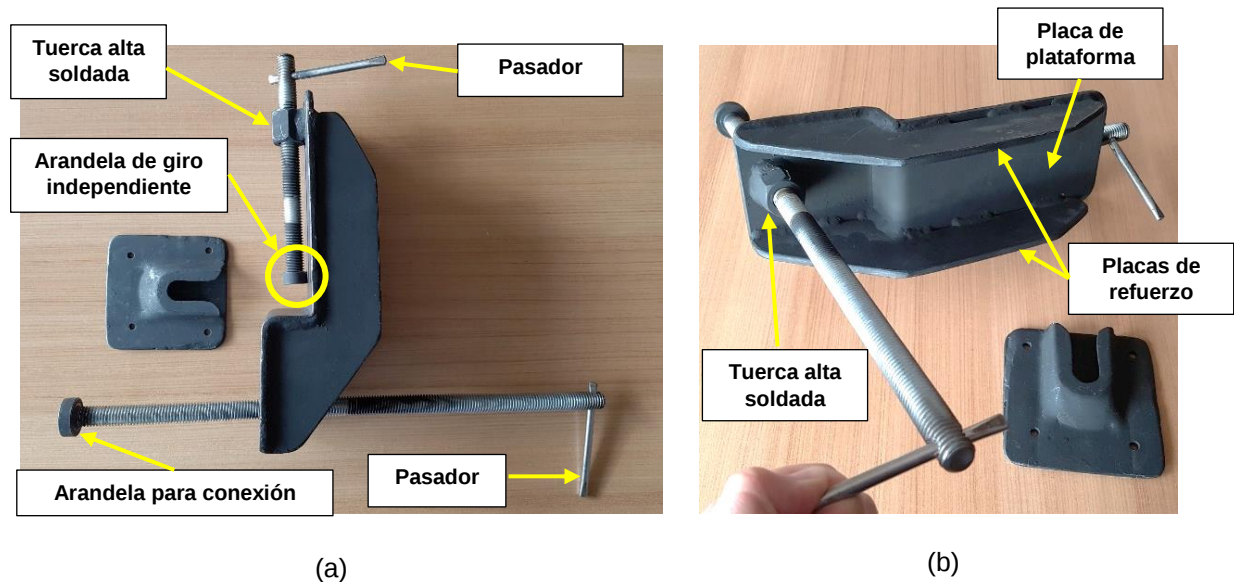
Fotografías de la versión final del prototipo fabricado: (a) vista en planta; (b) vista frontal en ángulo
